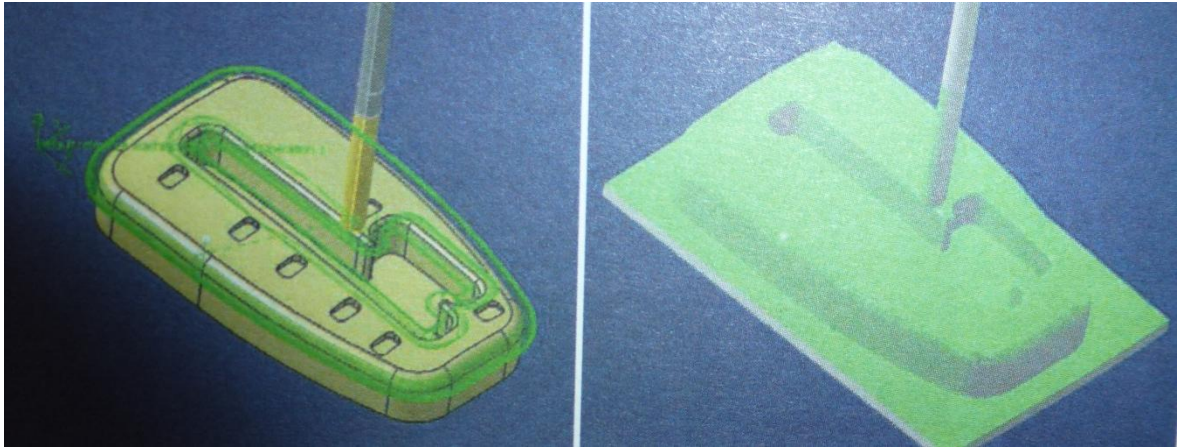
Vizualizace dráhy nástroje a obrobení tvaru nahrubo [10]
